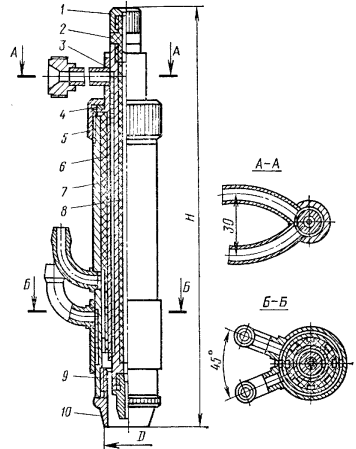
Сварочная горелка типа ГНА-315:
